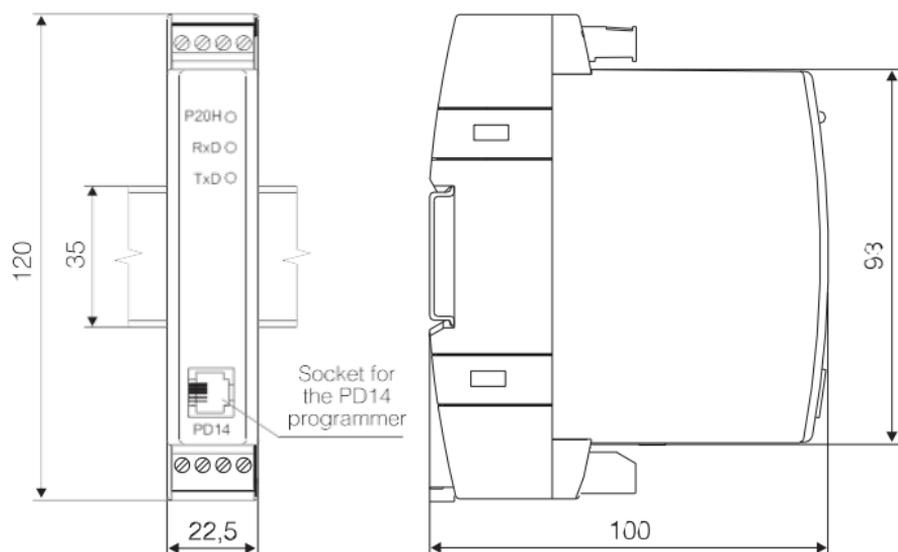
Dimensioni e montaggio del trasduttore PCE-P20H
